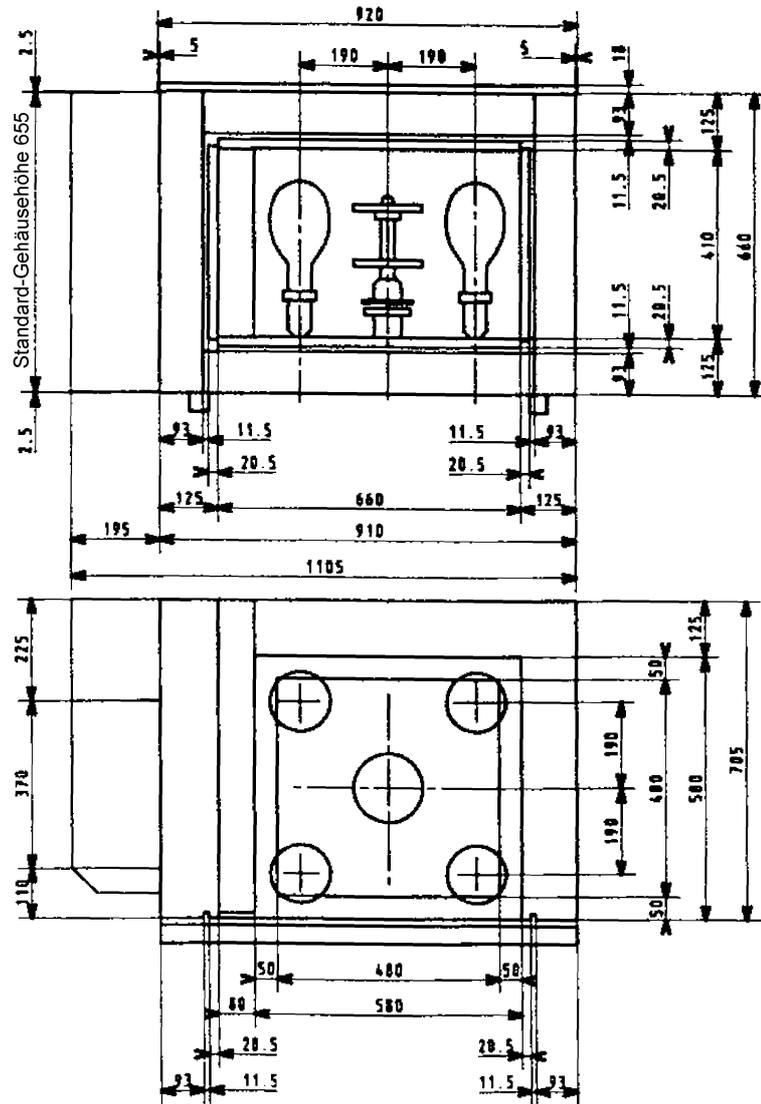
Prüfeinrichtung mit Quecksilberdampf Lampe: Konstruktionsdetails
